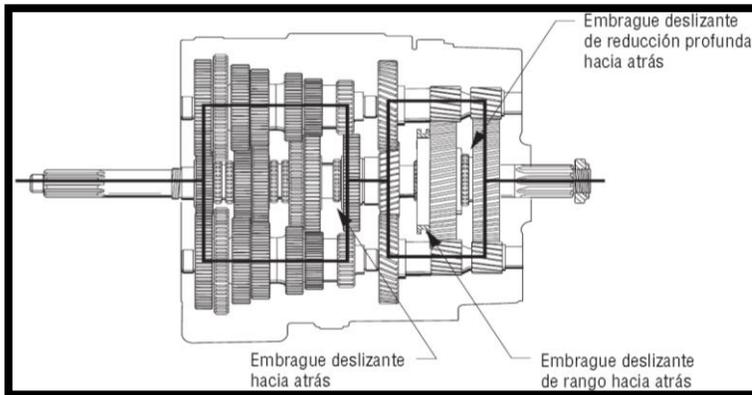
Engrane de reversa, transmisión tráiler: Fuente [34]
